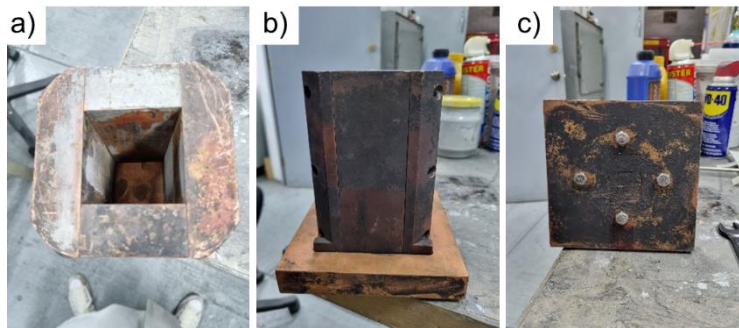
Molde metálico utilizado para obtener el acero LD: a) Vista superior, b) Vista lateral y c) Vista inferior. Las dimensiones del molde son 15.2x5.2x5 cm.
